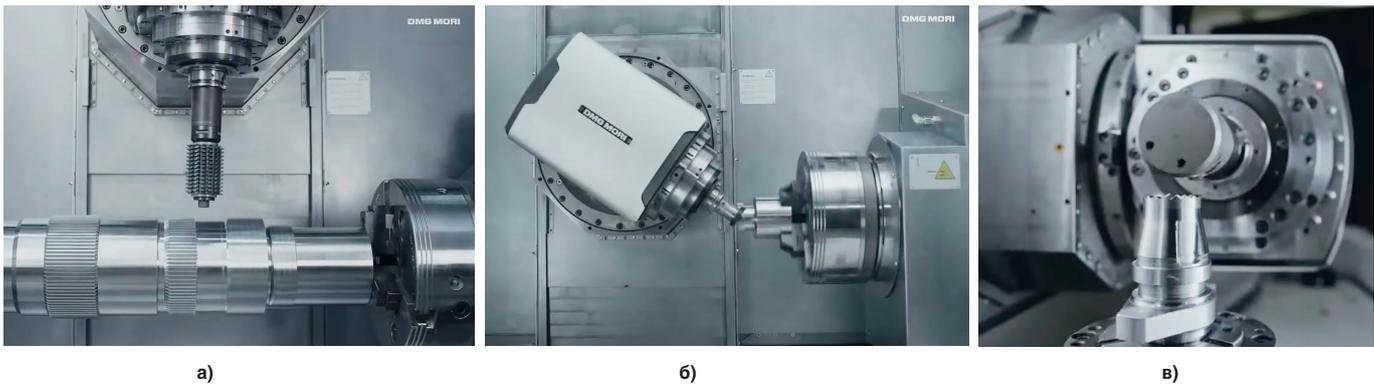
Методы зубообработки на универсальном оборудовании DMG MORI: а) GEAR HOBGING, б) GEAR SKIVING, в) CROWN HOBGING. Фотографии из видео: DMG MORI.
